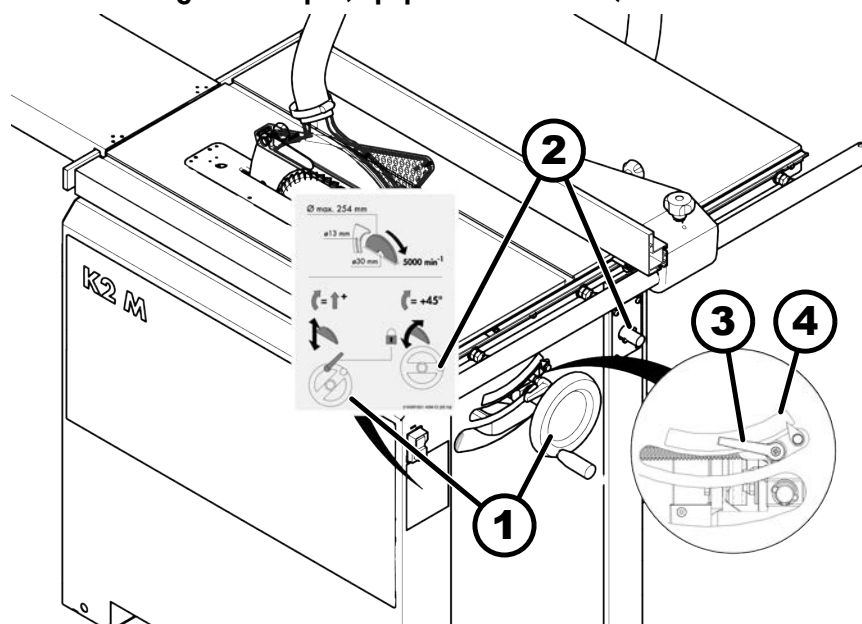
Réglage de la hauteur de coupe / de l'angle de coupe
